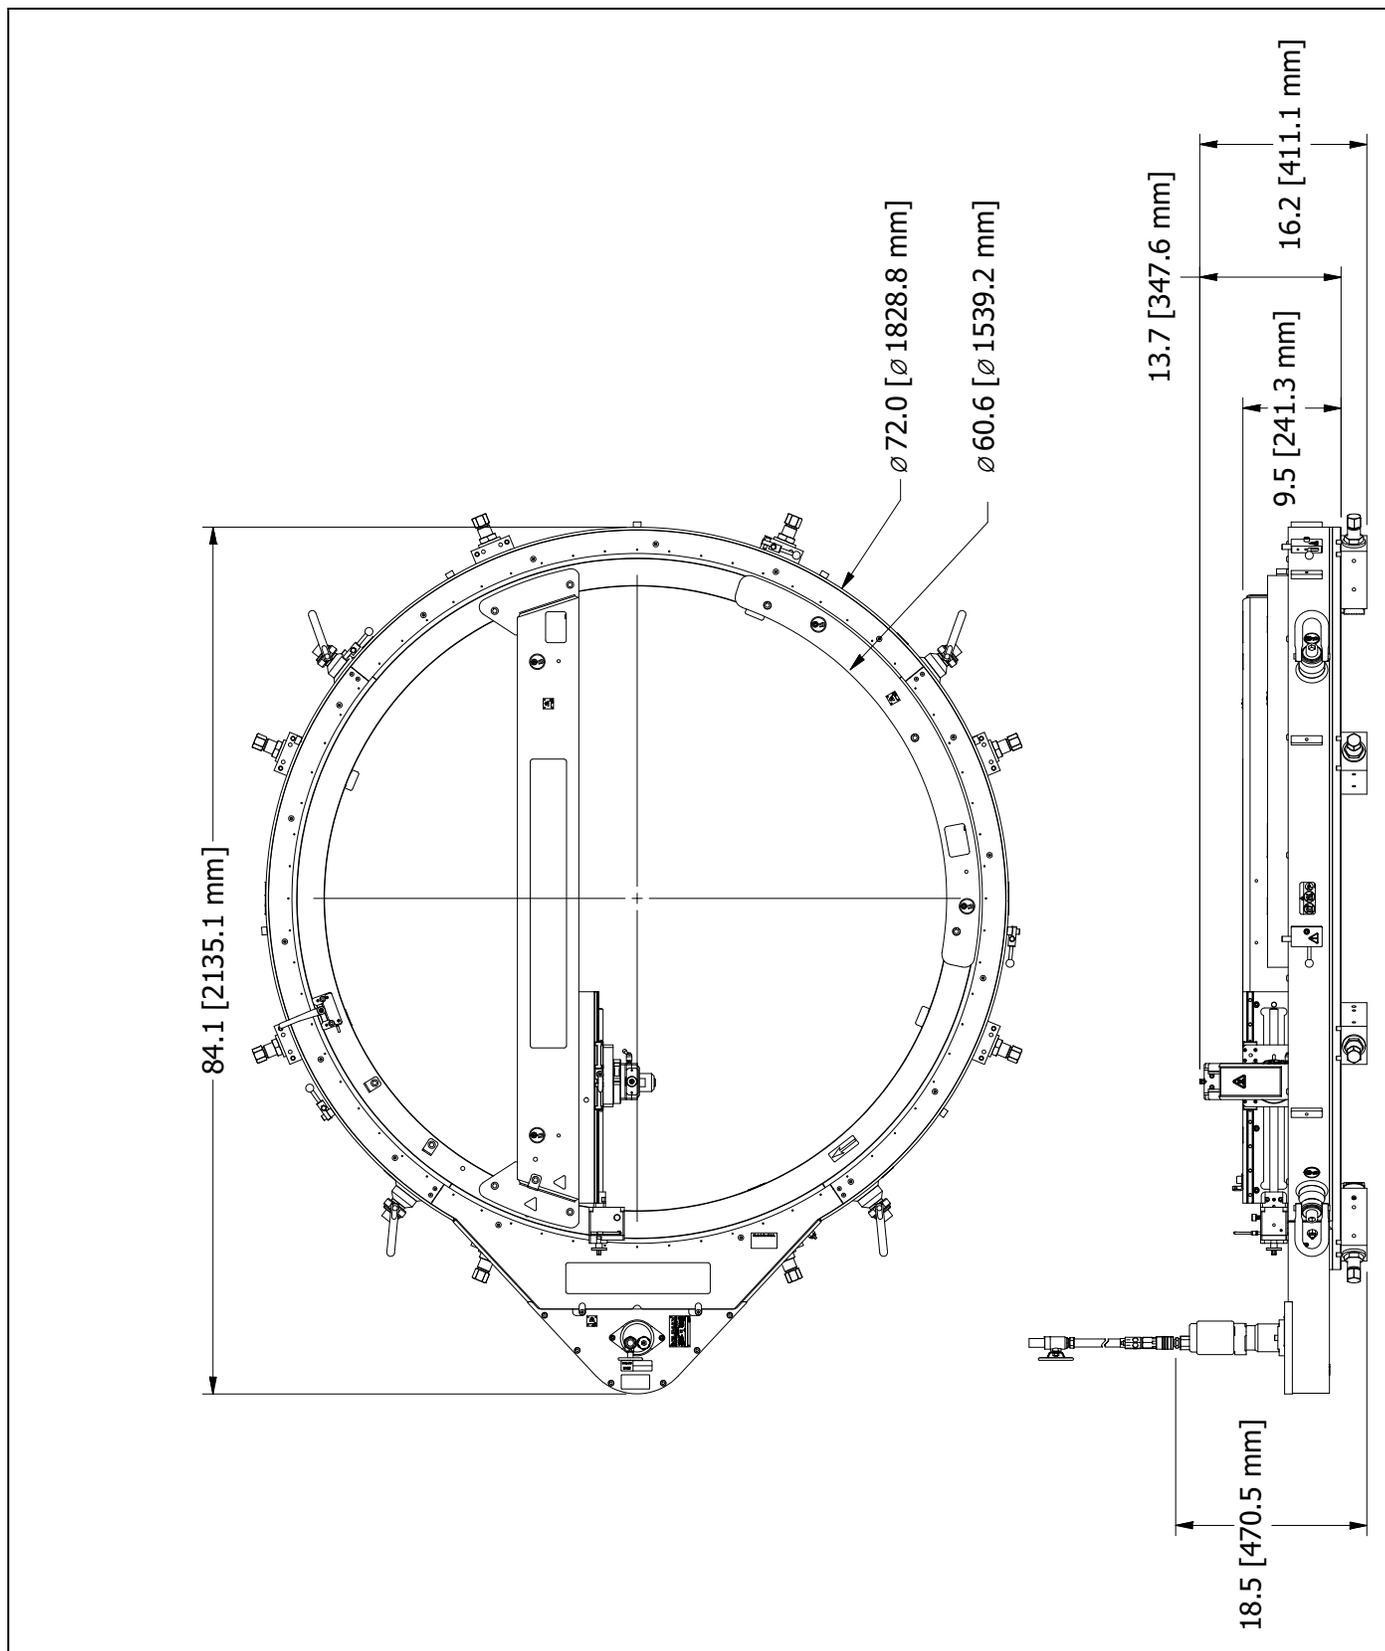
DIMENSIONS DE LA SURFACEUSE RAPIDE ODF60 SPEED FACER (RÉF. 86990)
